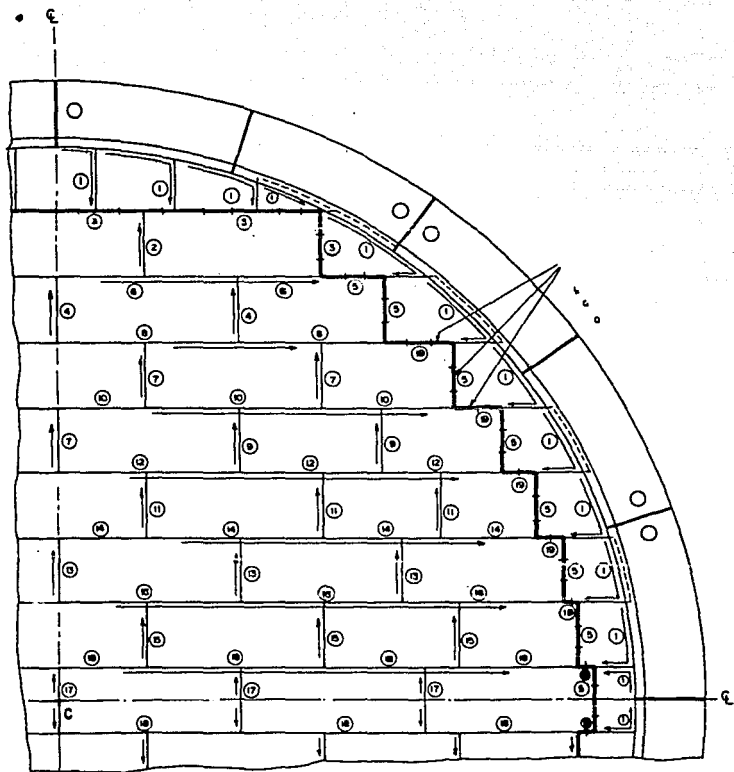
SECUENCIA DE SOLDADURA EN LAS PLACAS INFERIORES, RADIALES DEL PONTON.
